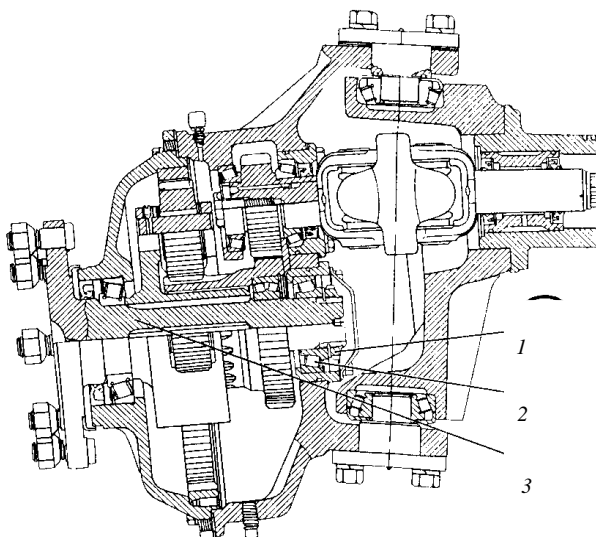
Проверка зазоров в подшипниках передних колес:
